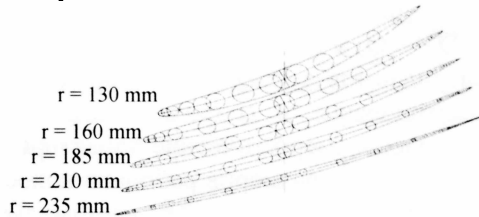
Профили лопасти рабочего колеса на различных радиусах
